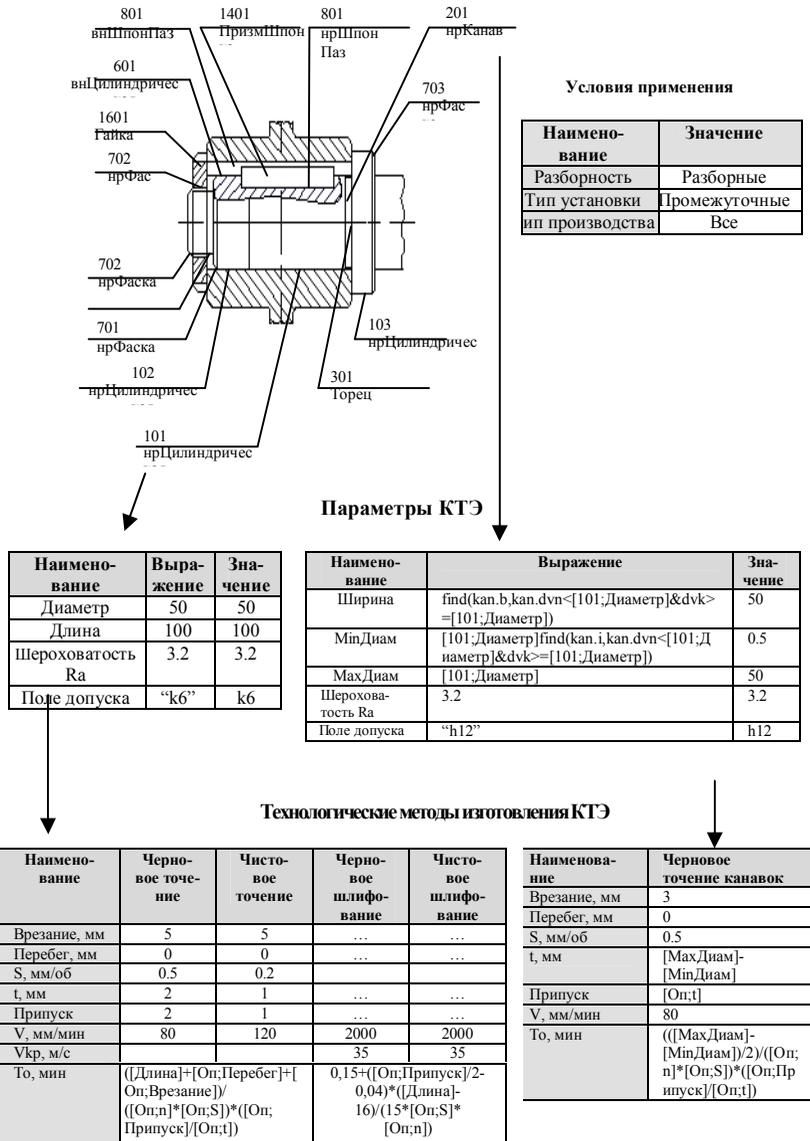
Пример формализованного представления сборочного соединения на примере шпоночного соединения с осевой затяжкой шлицевой гайкой
